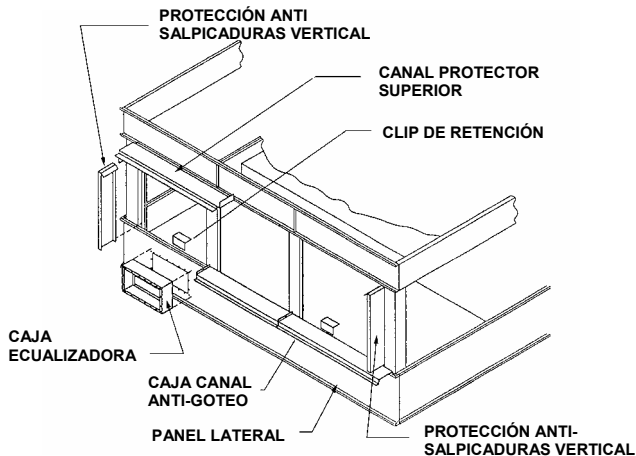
Canal Anti-Goteo y Protección Contra Salpicaduras para Modelos 4,9 – 5,3 y 7,3 Metros de Ancho
